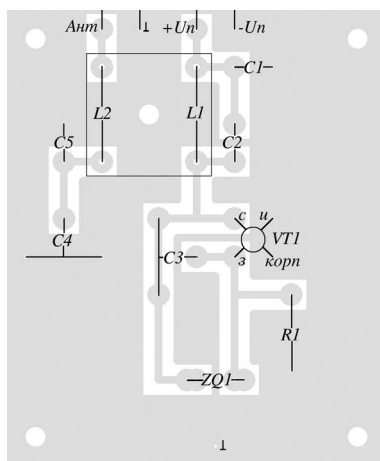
Эскиз монтажной платы передатчика. Вид со стороны расположения деталей
